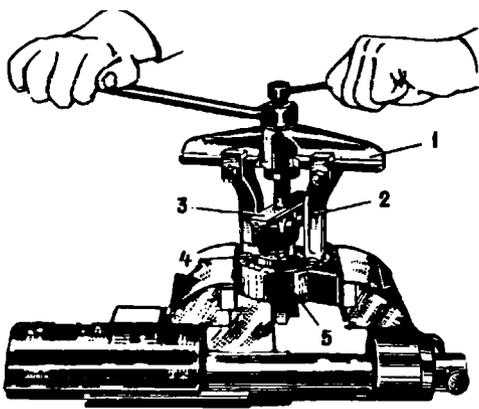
Выпрессовка подшипника из упругой опоры: 1 - планка А.40005/2; 2 - лапки А.40005/11; 3 - съемник А.40005/4; 4 - лапки; 5 - упругая опора
